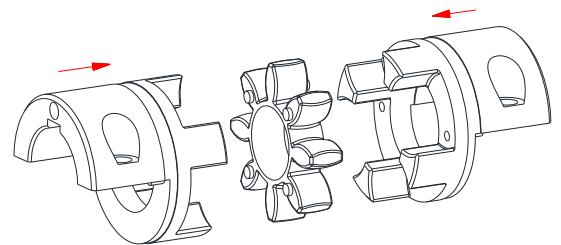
Montage der Nabengrundkörper, Zahnkränze und DKM-H-Mittelstück
